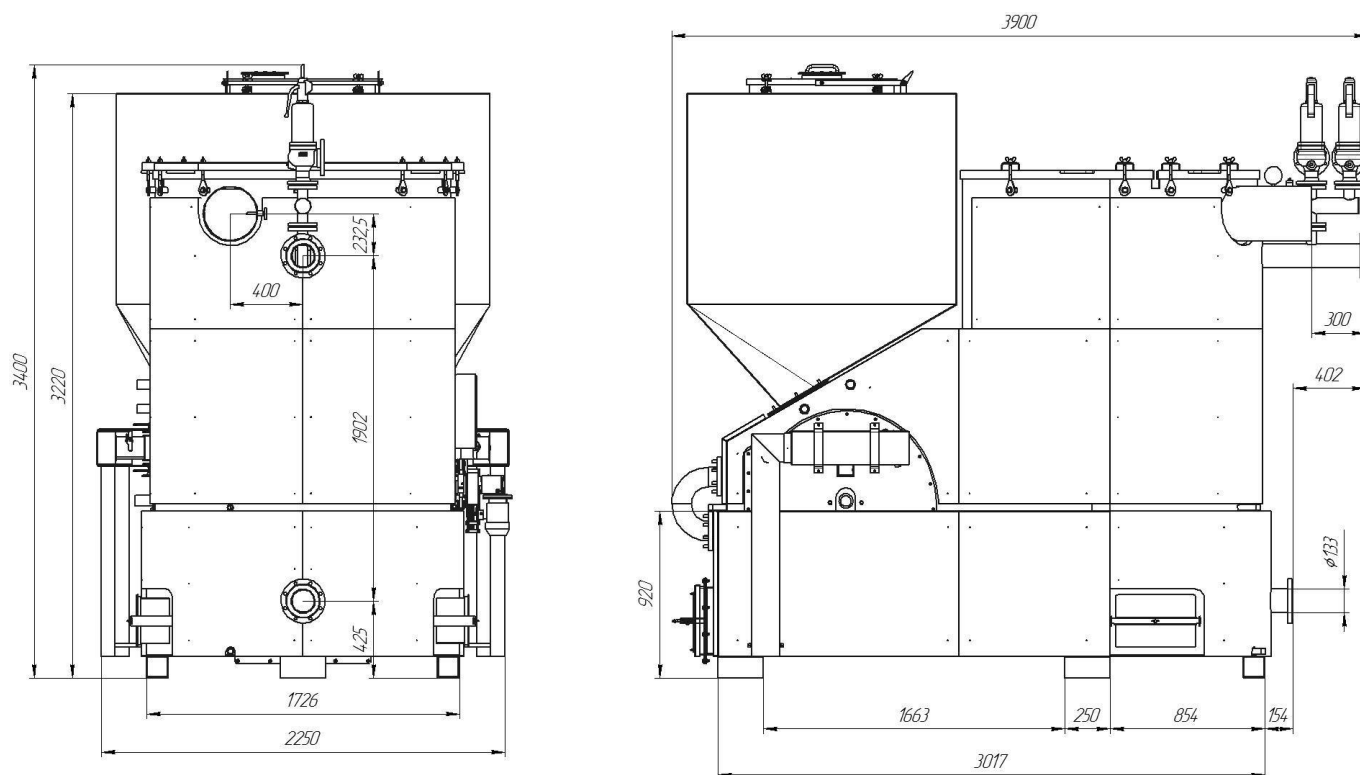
Эскизы котла Прометей-Автомат-1000М с габаритными размерами
